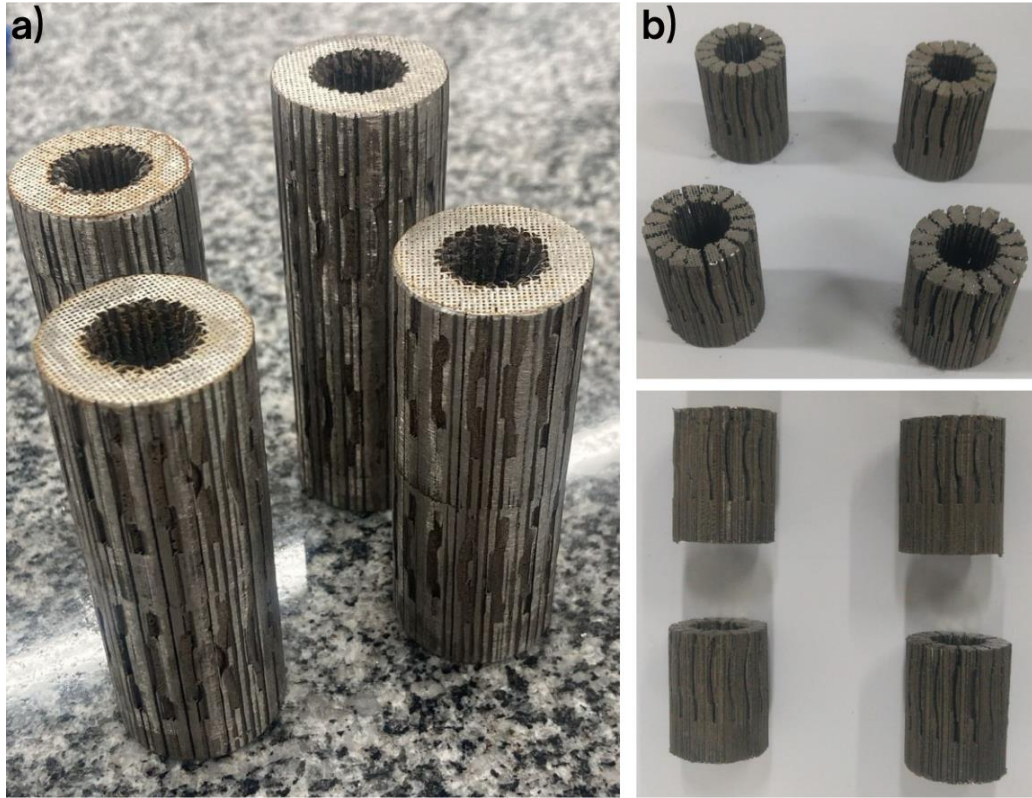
Protótipo do CMM fabricado por impressão 3D. Em a) Impressão final do CMM em quatro partes.
